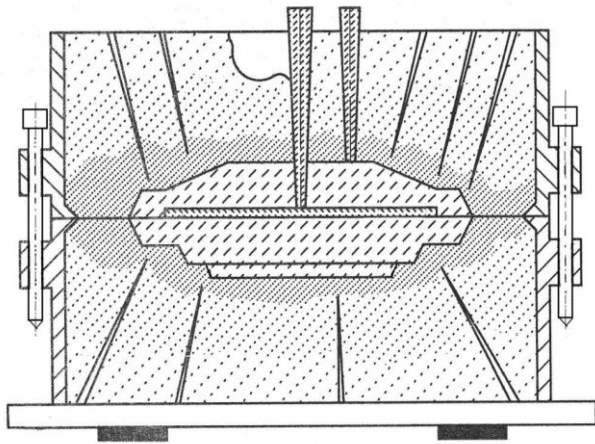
Formmuster mit Angussystem in geteilter Form
